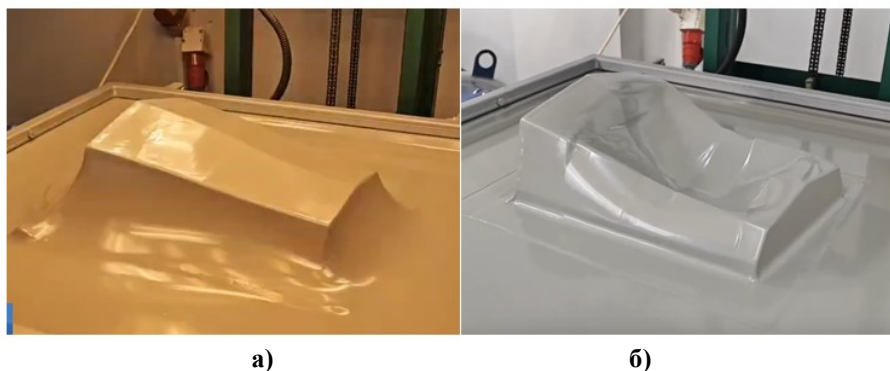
Вакуумная формовка поплавка на матрицу из PLA-пластика
